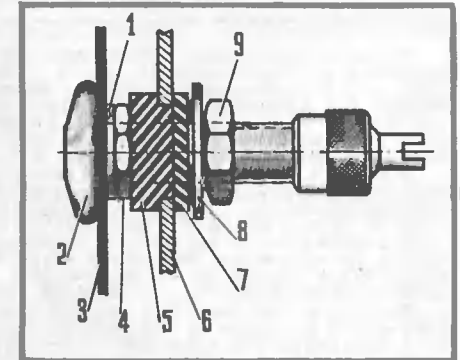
1 — текстолитовая шайба; 2 — вентиль; 3 — камера; 4 — внутренняя гайка; 5 — уплотнительная втулка; 6 — обод колеса; 7 — резиновая шайба; 8 — стальная шайба; 9 — гайка.
